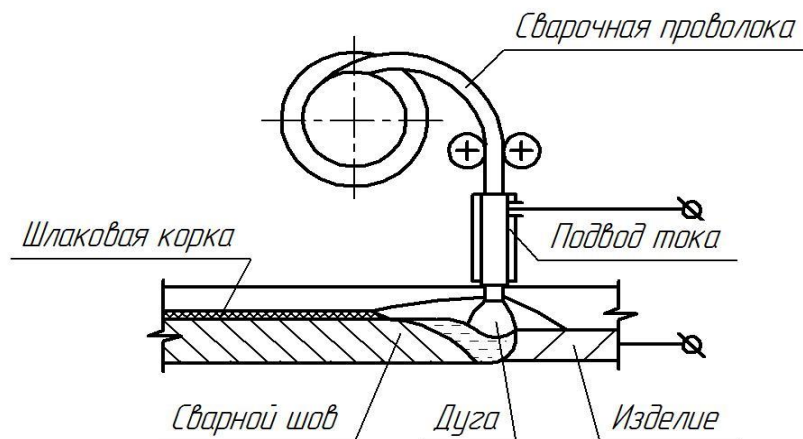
Схема выполнения сварки самозащитной порошковой проволокой
